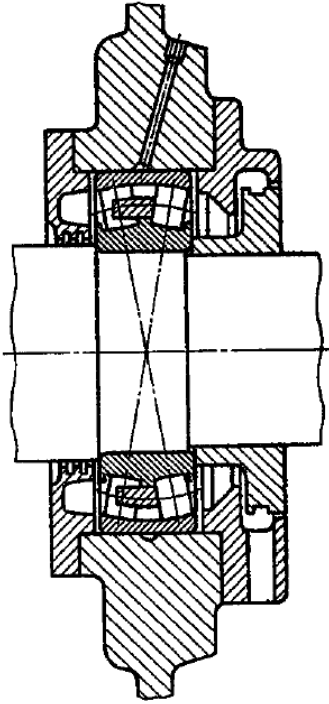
Підшипниковий вузол з каналом в корпусі для створення гідроспору та «плавання» зовнішнього кільця підшипника.
